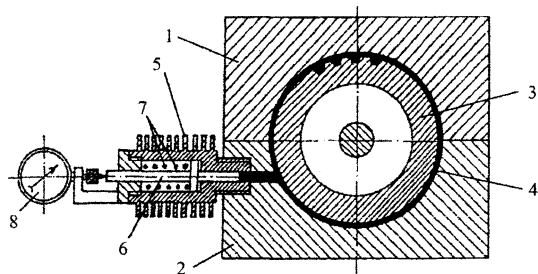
Схема измерения давления прессования: 1, 2 – верхняя и нижняя полуформы; 3 – зубчатый сердечник; 4 – заготовка ремня; 5 – манометр; 6 – шток; 7 – пружина; 8 – индикатор перемещений
